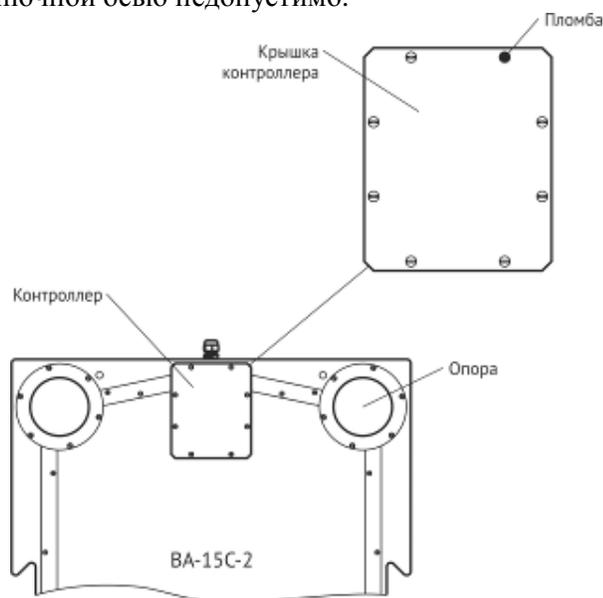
Схема нанесения знака поверки на весах ВА-15С-2 и ВА-15С-2М
